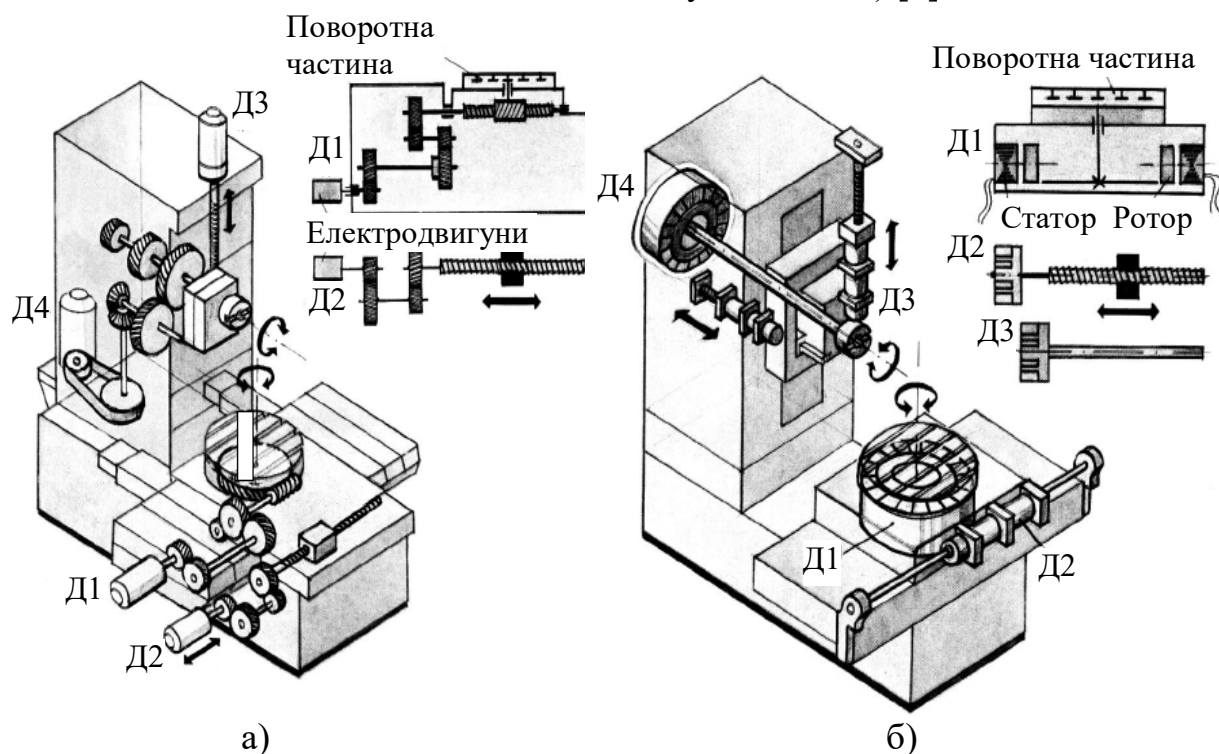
Металорізальні верстати: а – з механічними приводами; б – з мехатронними приводами
